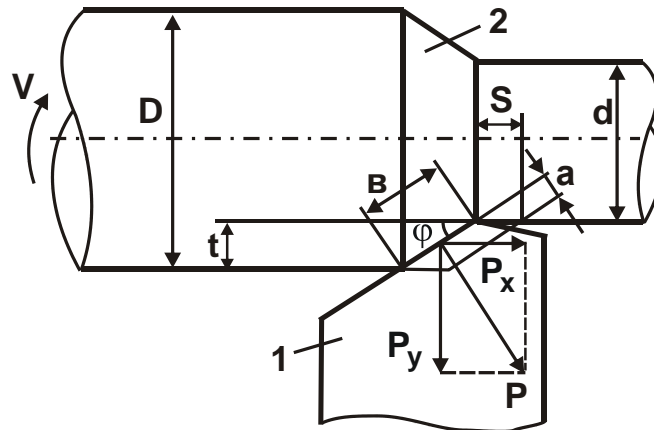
Расчетная схема продольного точения: 1 – резец; 2 – деталь; D, d – диаметры заготовки и обработанной детали
